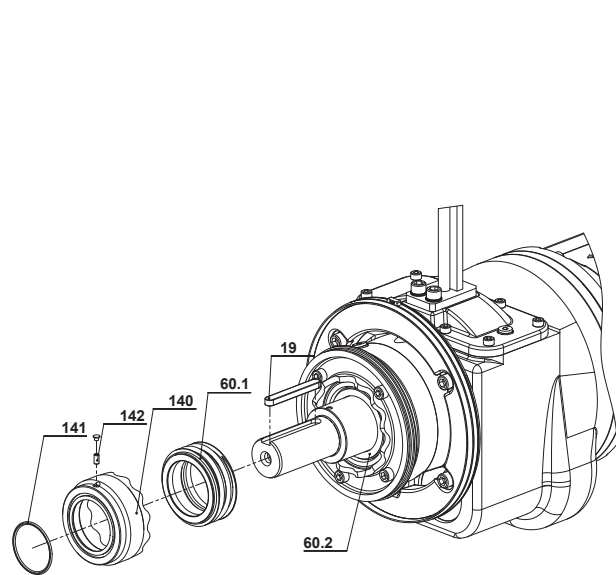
Desmontaje/colocación de la junta mecánica XSB 900, 2500
